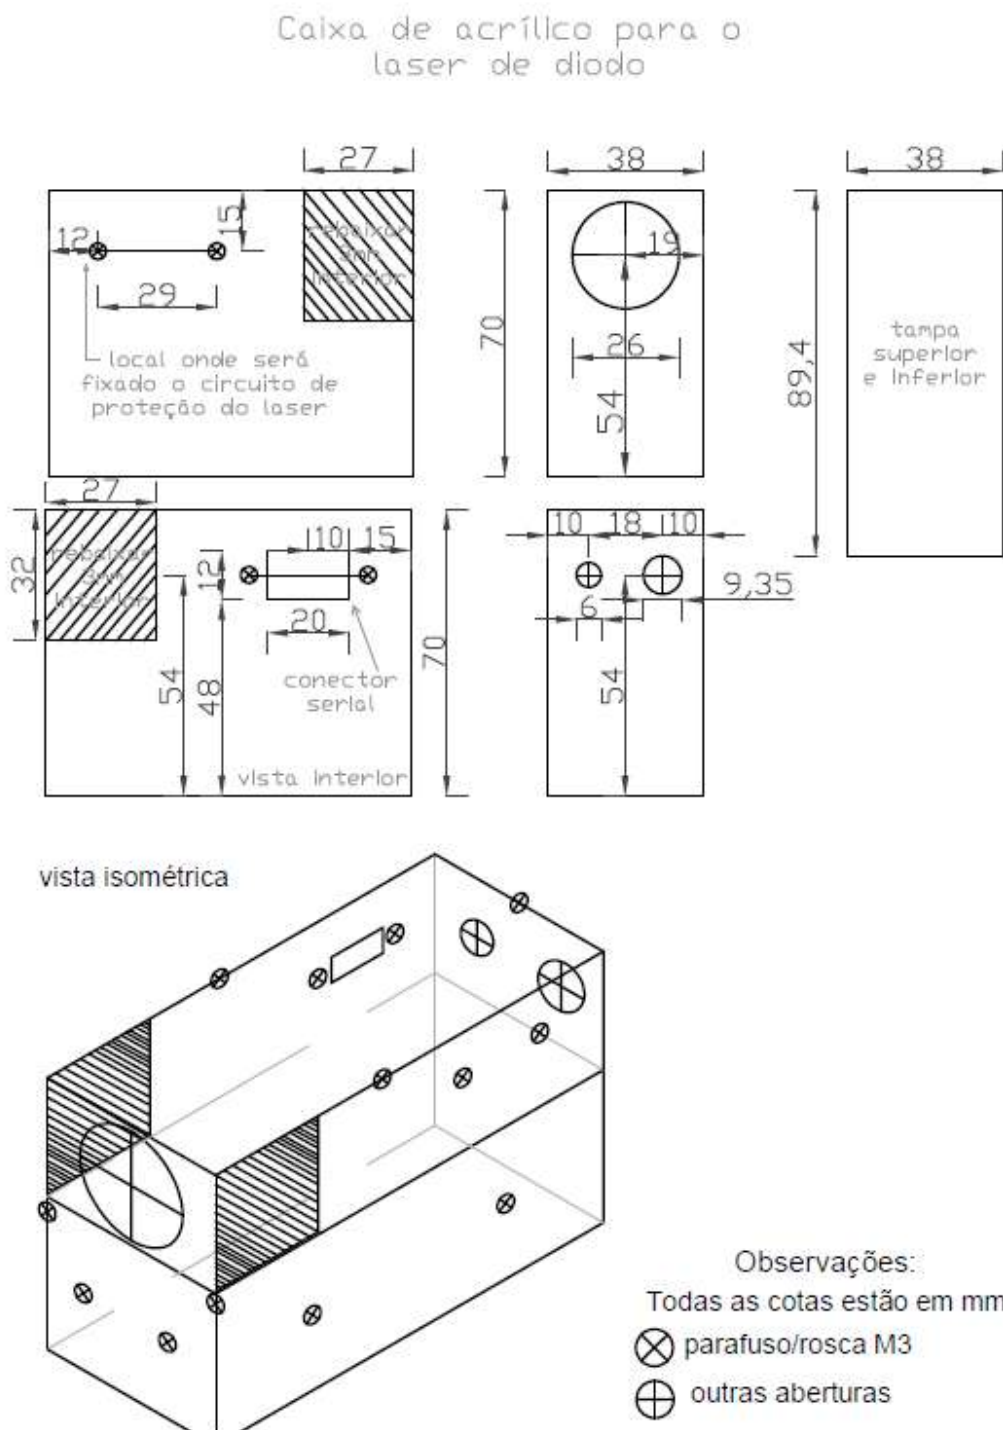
Design e dimensões para a caixa de acrílico do Laser. Fonte: (ALVES, 2019).
